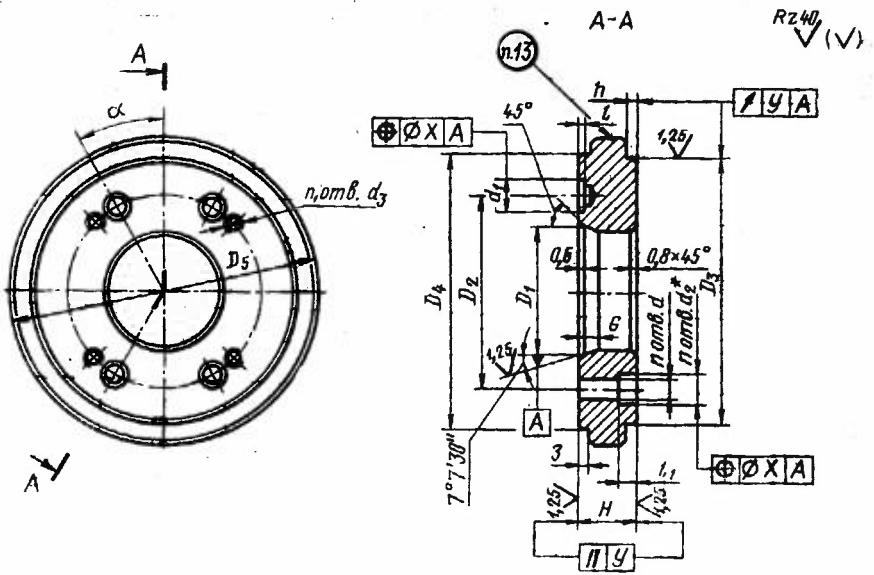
Промежуточный фланец на фланцевый конец шпинделя станка
